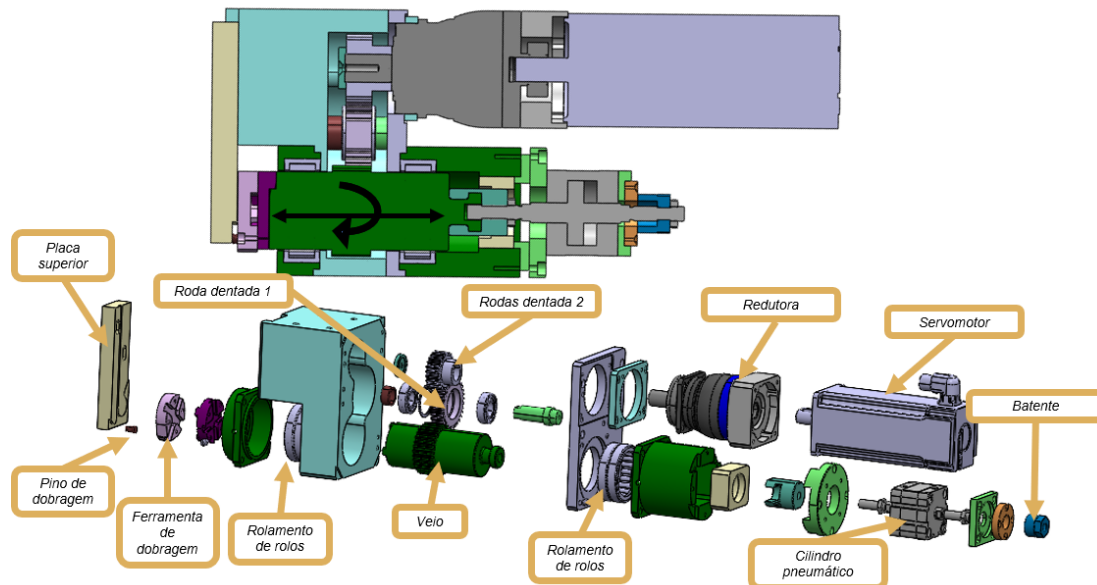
Vista explodida do sistema de dobragem do gancho e pré dobra
